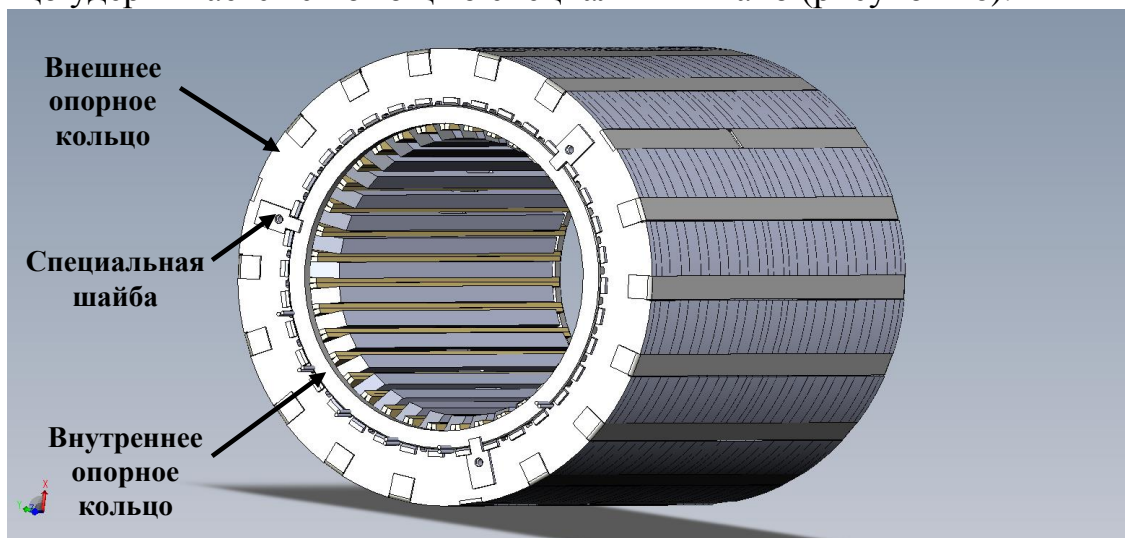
Магнитная система якоря асинхронного двигателя с кольцевыми обмотками в сборе
